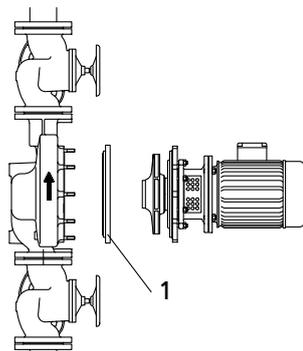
Horizontaler Einbau mit Blindflansch (1 = Blindflansch, Zubehör)
